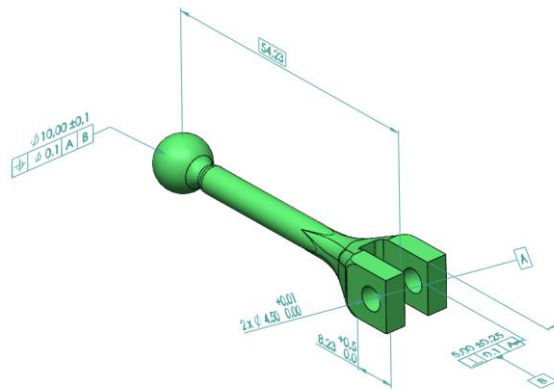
Tolerancias dimensionales "Barra 3" pulgar
